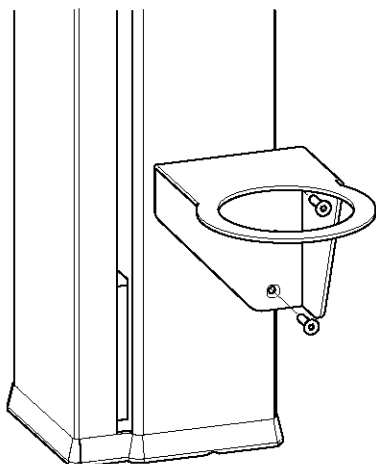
Установка держателя для фильтровальной ячейки или дозатора Dosino
